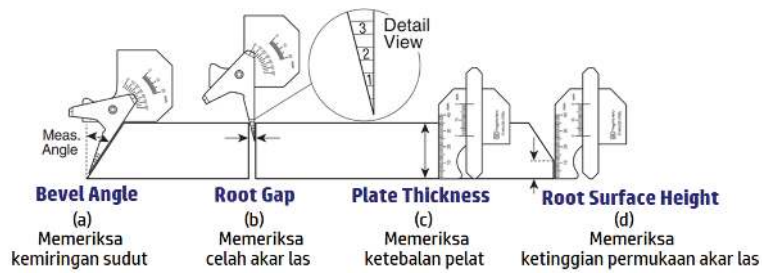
Penggunaan *Hi-Lo Welding Gauge
